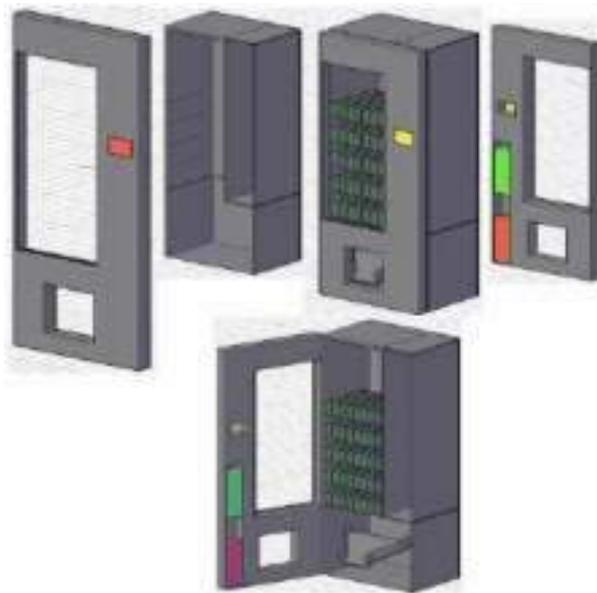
Modelo en 3D de las partes mecánicas de la máquina.
